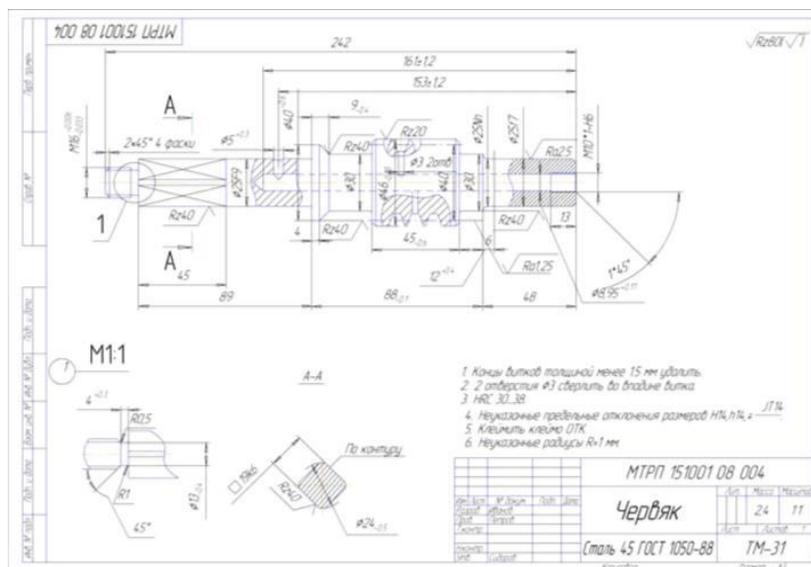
Чертеж детали, выполненный в САПР КОМПАС
